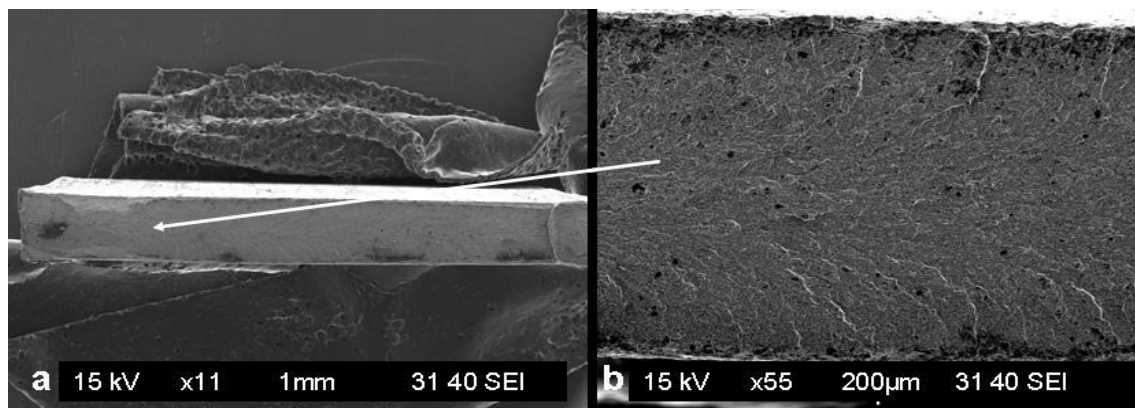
(a) Vista total de la superficie de fractura (b). aspecto de la fractura frágil con lo que asemeja marcas de Chevron.
